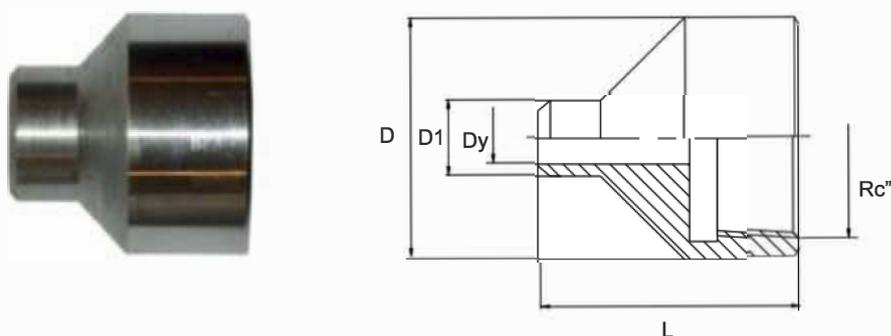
Муфта переходная для соединения РВД с трубопроводом
